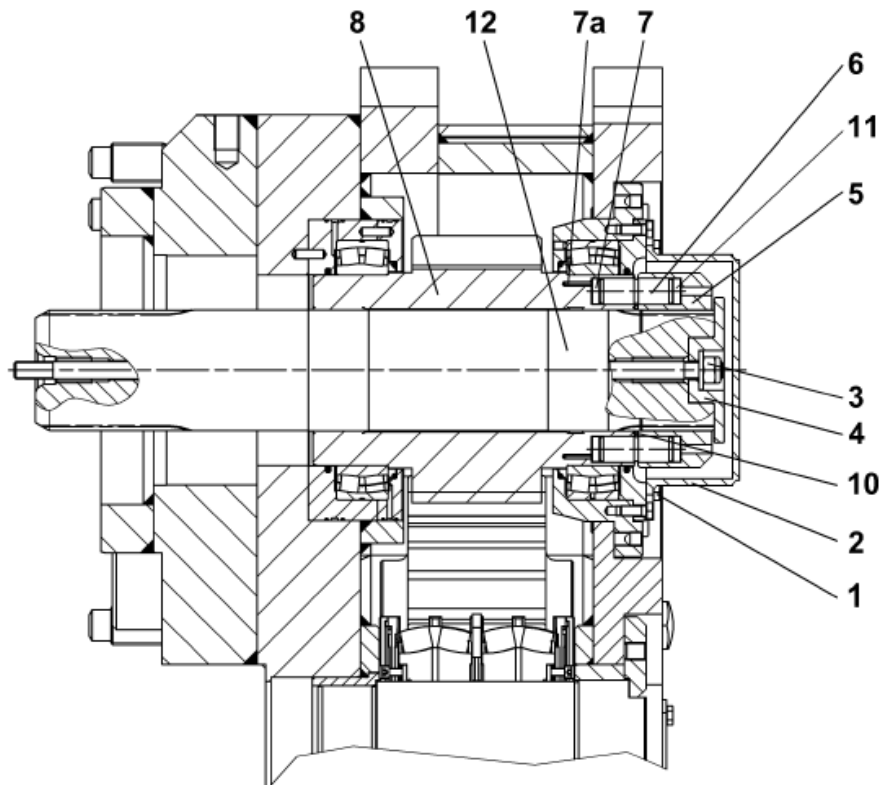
Предохранительная муфта цевочно-реечного механизма подачи
